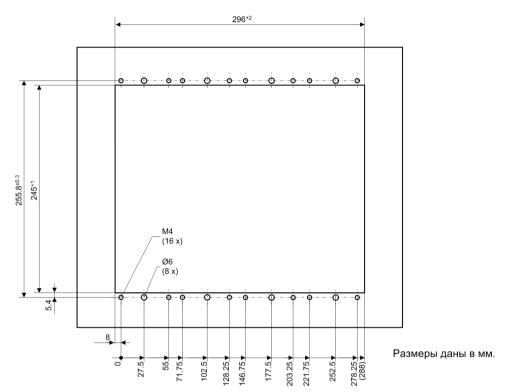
Ширина вырезов и схема сверления отверстий – устройство 1/3, второй ряд устройств
